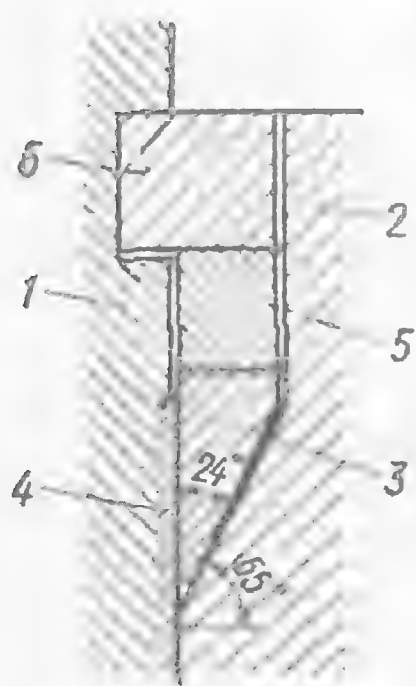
Самоуплотняющееся соединение корпуса с крышкой конструкции фирмы Роквелл-Эдвард (США).
